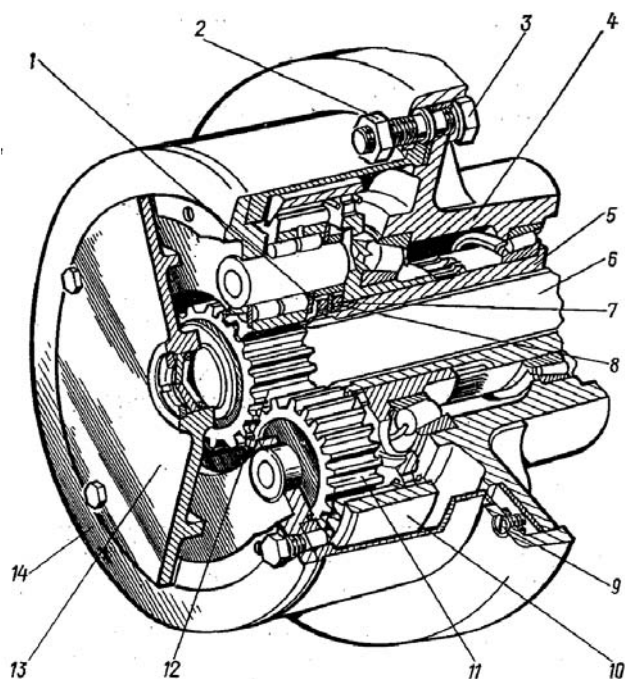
Колесный редуктор: 1 — контргайка; 2, 3, 7 — гайка; 4 — картер; 5 — ступица; 6 — полуось; 8 — шайба стопорная; 9 — винт; 10 — шестерня эпициклическая; 11 — сателлит; 12 — шестерня солнечная; 13 — крышка; 14 — водило
